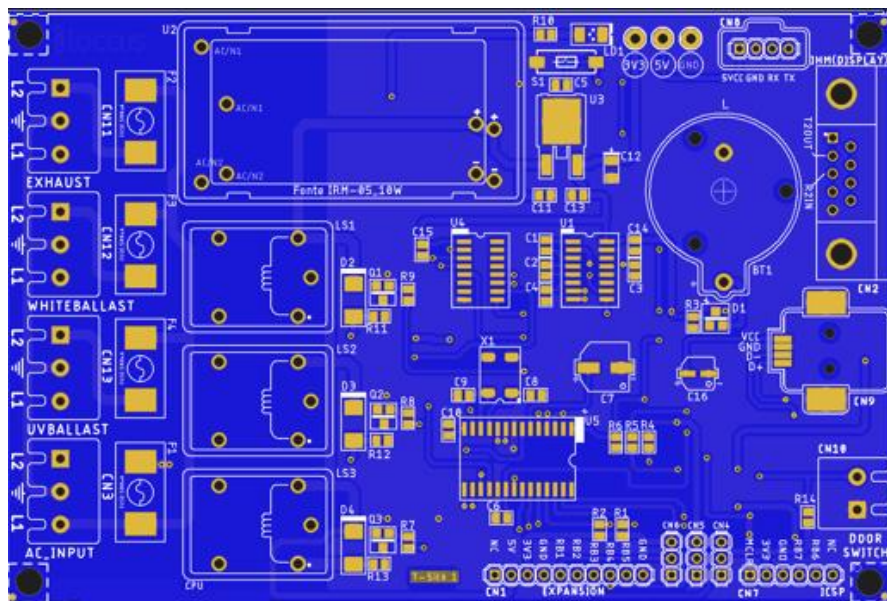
Layout Superior da Placa de Circuito Impresso.
